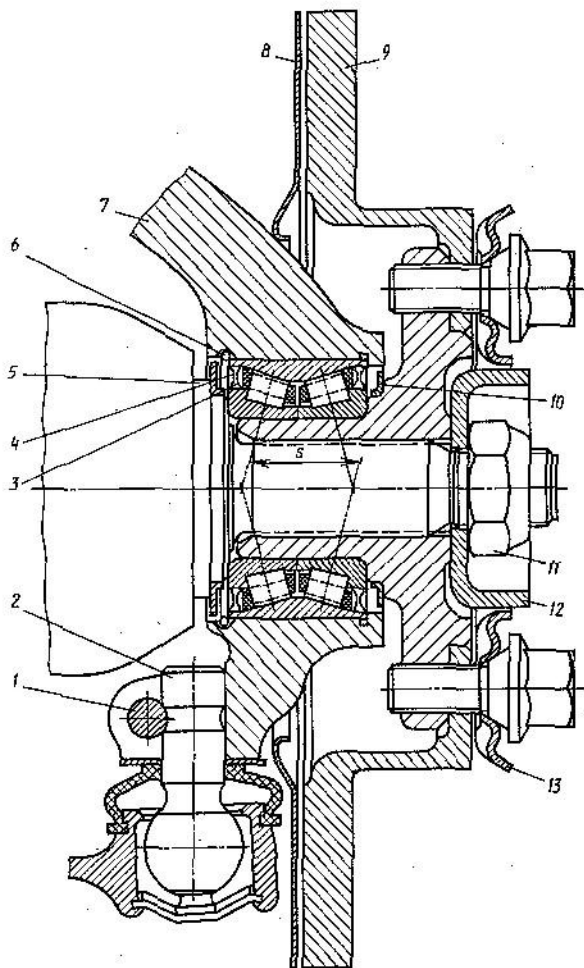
Фирма «Рено» предусматривает на передних колесах моделей 9 и 11 с дизельным двигателем двухрядный конический роликовый подшипник со смазочным материалом на весь срок службы. Хорошо видно фиксирование наружного кольца проволочным стопорным кольцом 6 и короткая опорная база 8. Уплотнение с обеих сторон осуществляется скользящими по внутренним кольцам уплотнительными кольцами 3 совместно с центробежными отражателями 4, скользящими по бортикам наружного кольца. Кроме того, имеются центробежные отражатели 5 и 10, напрессованные на неподвижный шарнир и на ступицу, которые образуют лишь небольшой зазор относительно отверстия в опоре 7 подшипника колеса и служат для предварительного уплотнения. Ступица с предварительно установленным на ней коническим роликовым подшипником с помощью гайки 11 сажается на вал и затягивается установленным моментом. Колпачковая шайба 12 служит для грубого центрирования при установке дискового колеса 13. Шаровой палец нижнего направляющего шарнира входит в цилиндрическое отверстие и фиксируется поперечным болтом 1. Тормозной диск 9 устанавливается на ступице снаружи и прикрывается с внутренней стороны брызговиком 8
